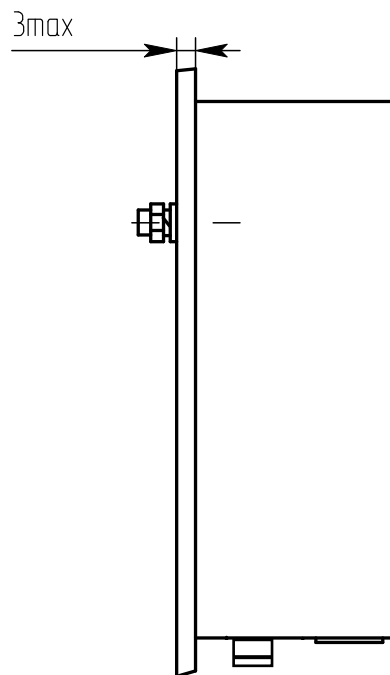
Крепление со стороны боковой стенки кожуха
